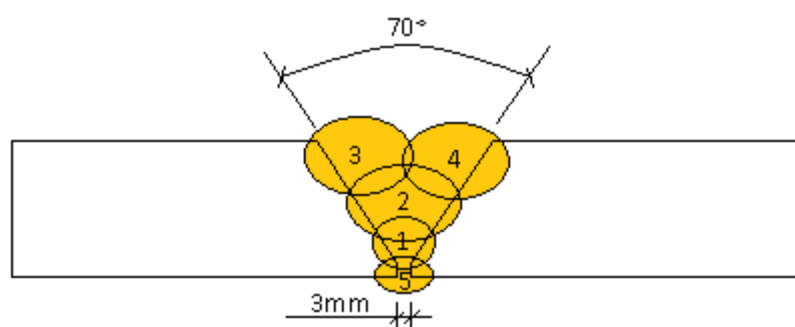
Esquema utilizado na soldagem pelo processo SMAW.
